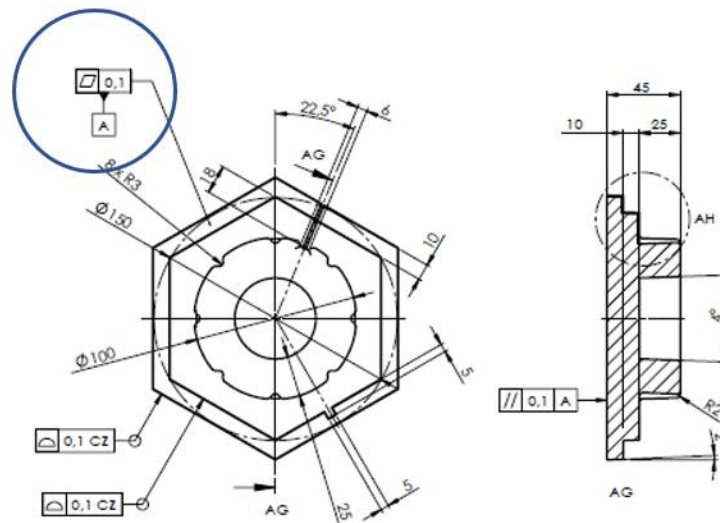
Tolerancia de Planitud de Presa tipo O
